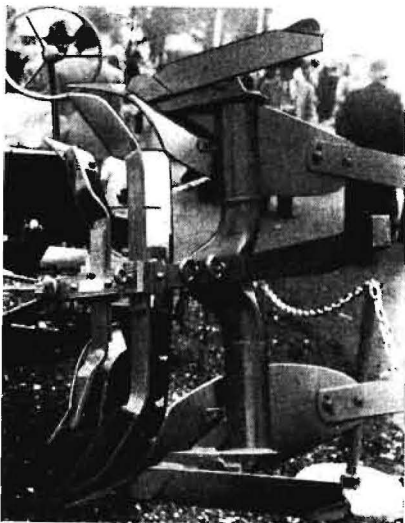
Pflugkörper, gebildet aus einem hohlen Stahlgußstück und einem angeschweißten Ovalrohr
